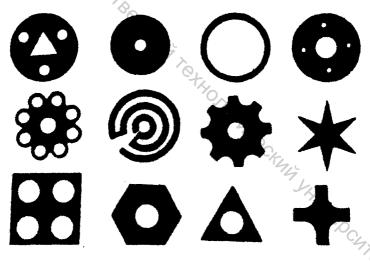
Заготовки, полученные дискретной прокаткой
